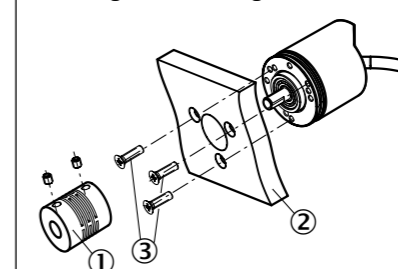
Anbau DBS36 Klemmflansch über flanschseitige Gewindebohrungen
